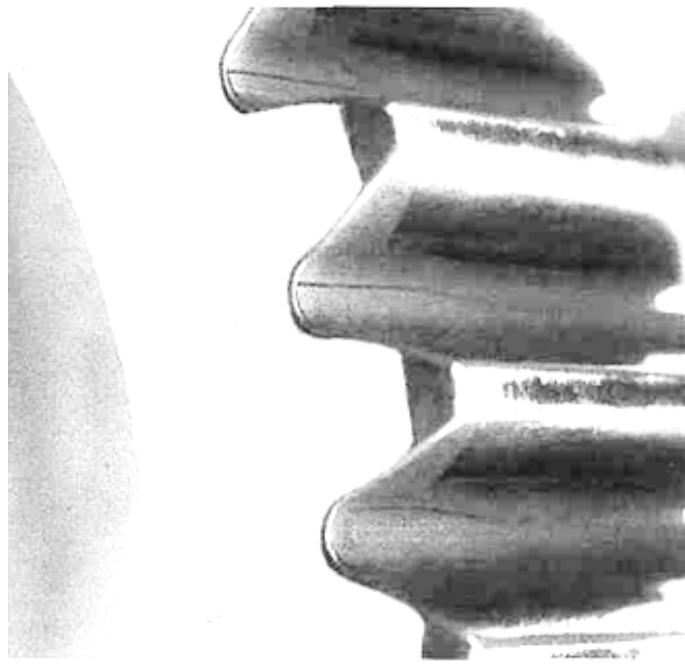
Шлифовочные трещины во впадинах зубчатого колеса.
